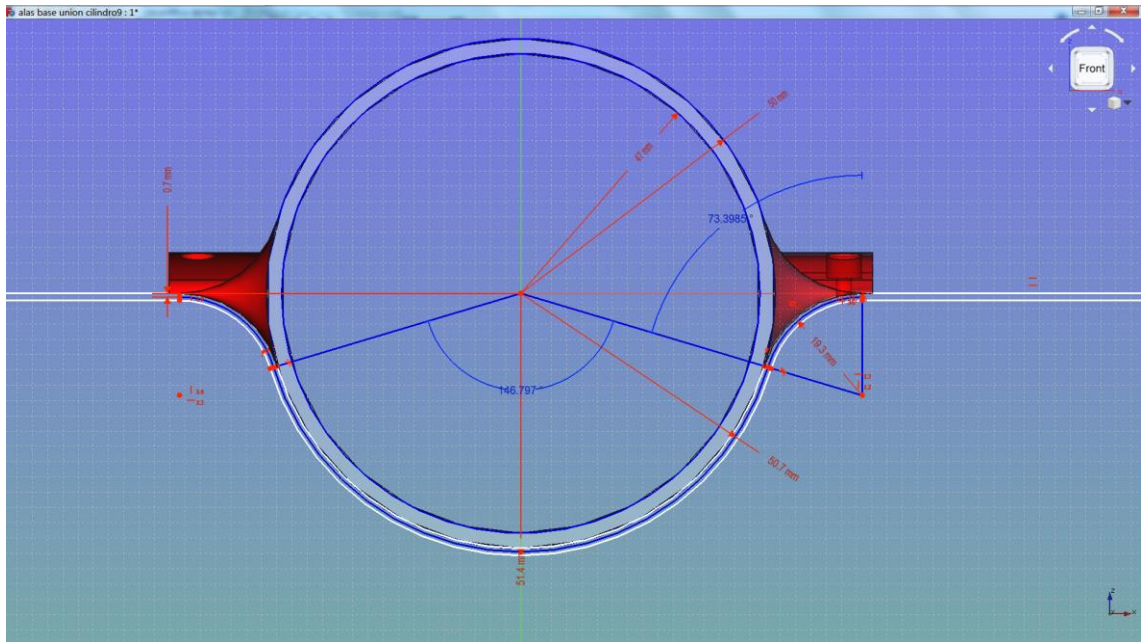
Vista frontal entre pieza adaptación alas y cilindro. Fuente Propia.
